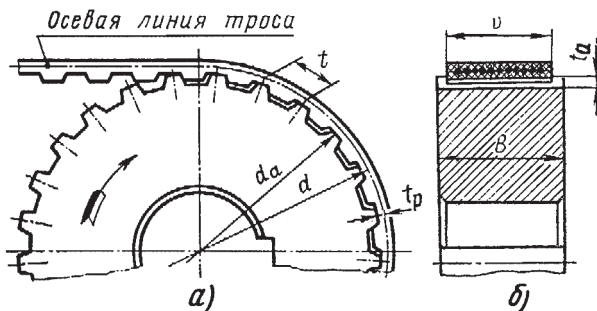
Основные параметры передачи зубчатым ремнем
